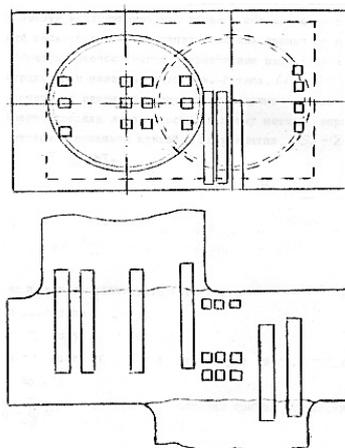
Схема вырезки заготовок для усталостных испытаний из секции коленчатого вала
